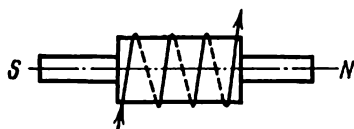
Spires enroulées sur le tambour de rotor d'un turbo-alternateur pour démagnétiser l'arbre
